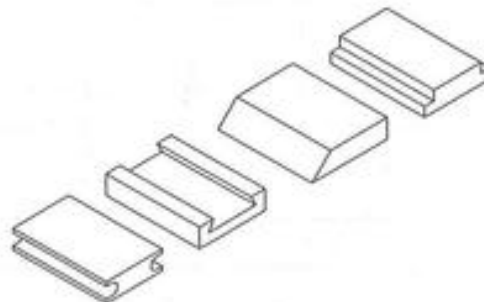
Piezas fabricadas por mortajado o cepillado.
